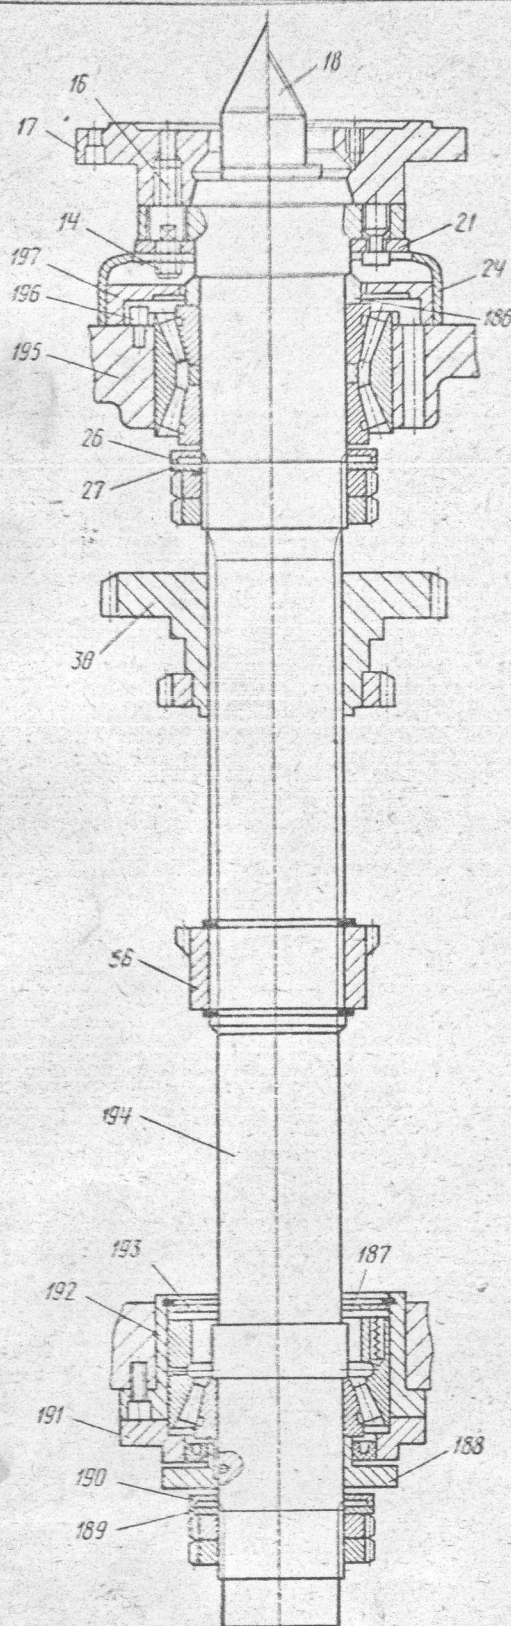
Шпиндельная бабка (чертеж шпинделя в сборе)
